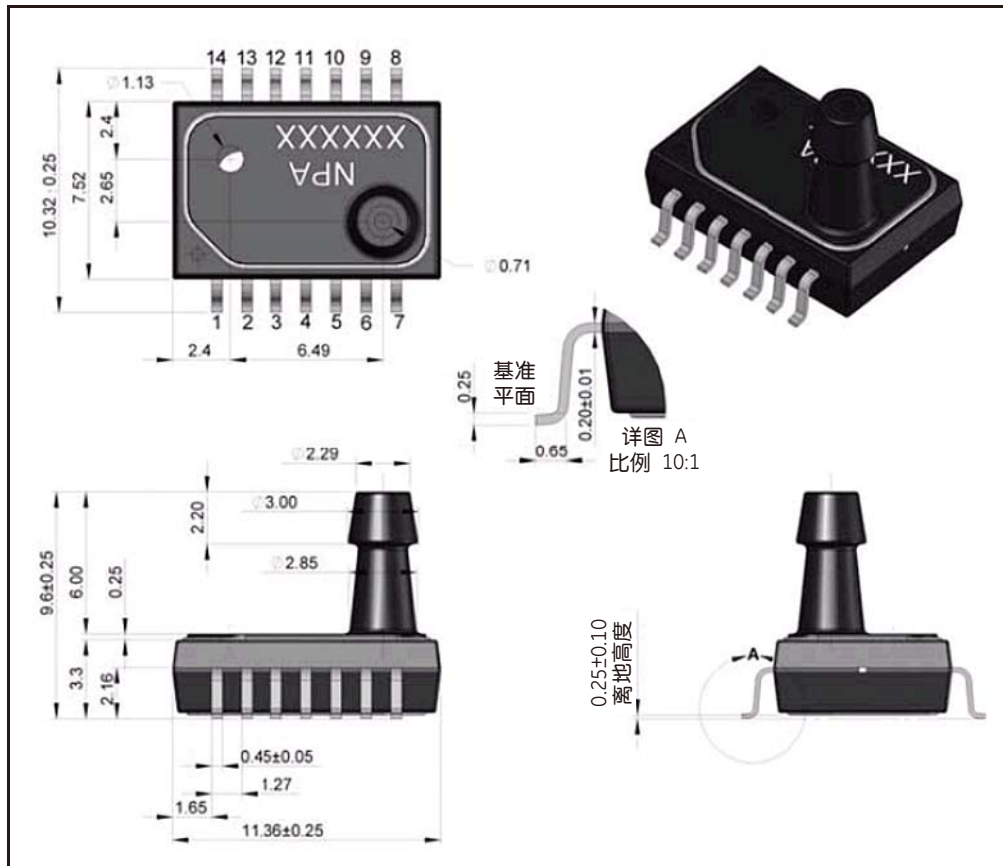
传感器封装尺寸 (mm) - 带倒扣的压力接口设计
